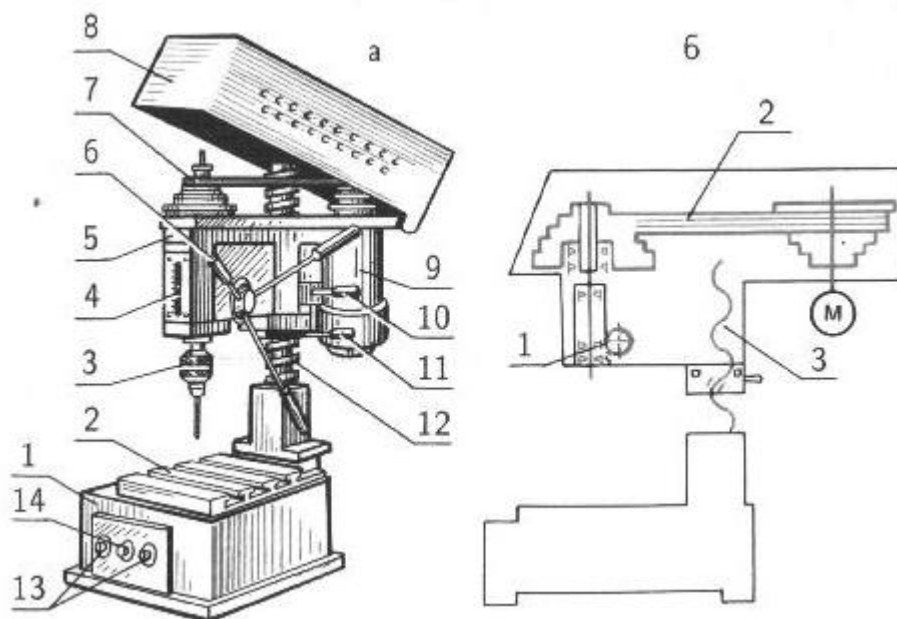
Общее устройство (а) и кинематическая схема (б) сверлильного станка
